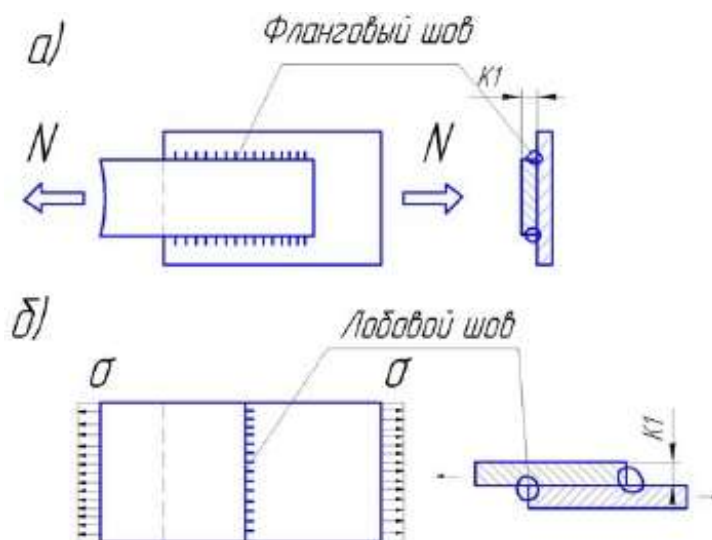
Фланговый (а) и лобовой (б) сварные швы
